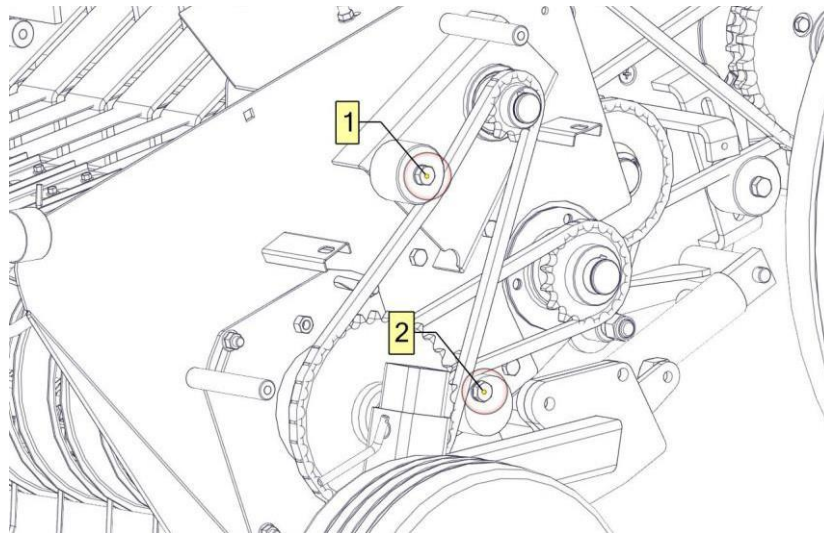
Регулировка натяжения цепей подборщика (левая сторона)
